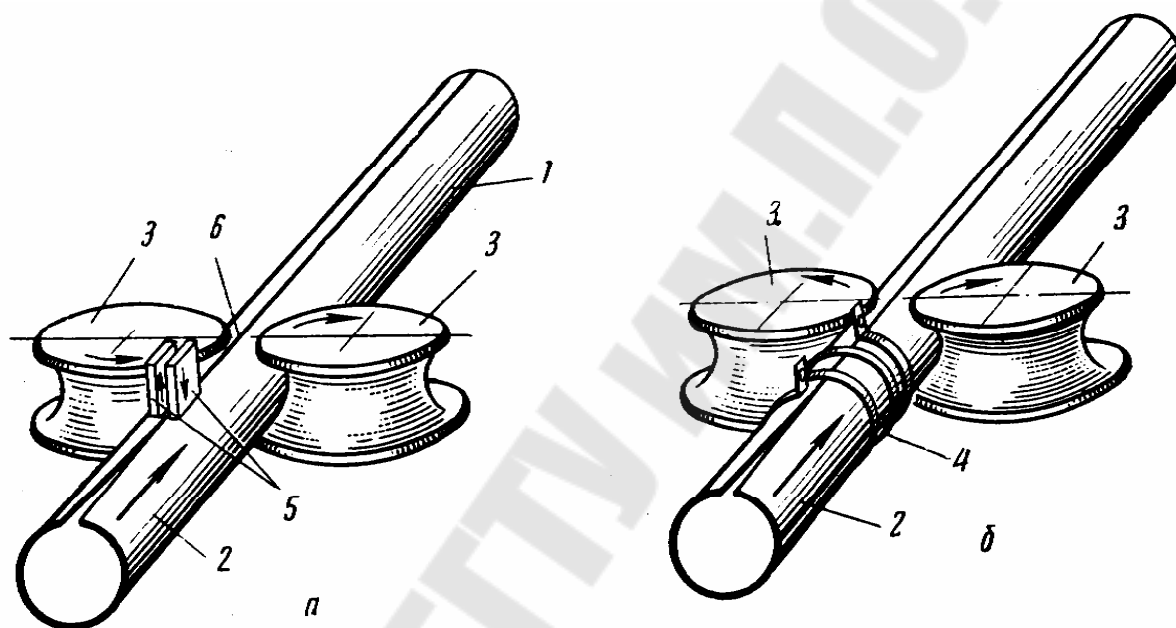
Схема подвода тока высокой частоты к кромкам трубной заготовки: 1 – сваренная труба; 2 – сформованная заготовка; 3 – сварочные валки; 4 – индуктор; 5 – скользящий контакт; 6 – место сварки
